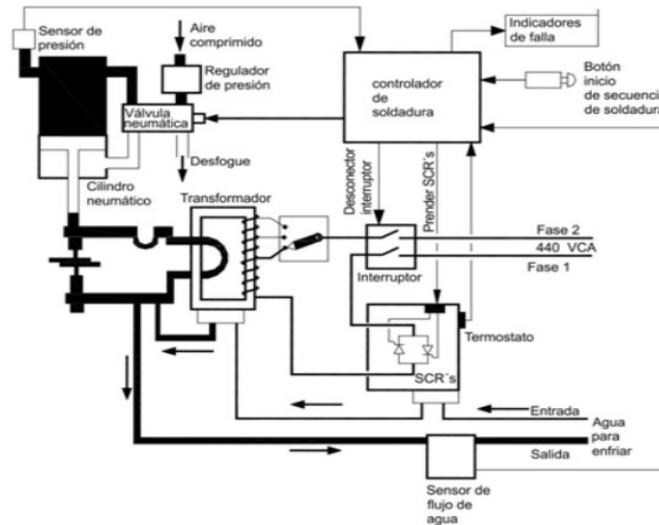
Esquema general de una máquina de soldadura por puntos
